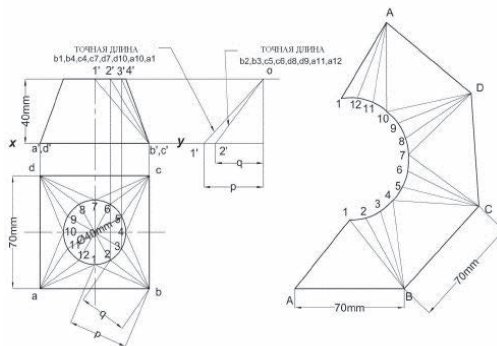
Переходной элемент трубопровода для соединения прямоугольной трубы с трубой круглого сечения. [1]
